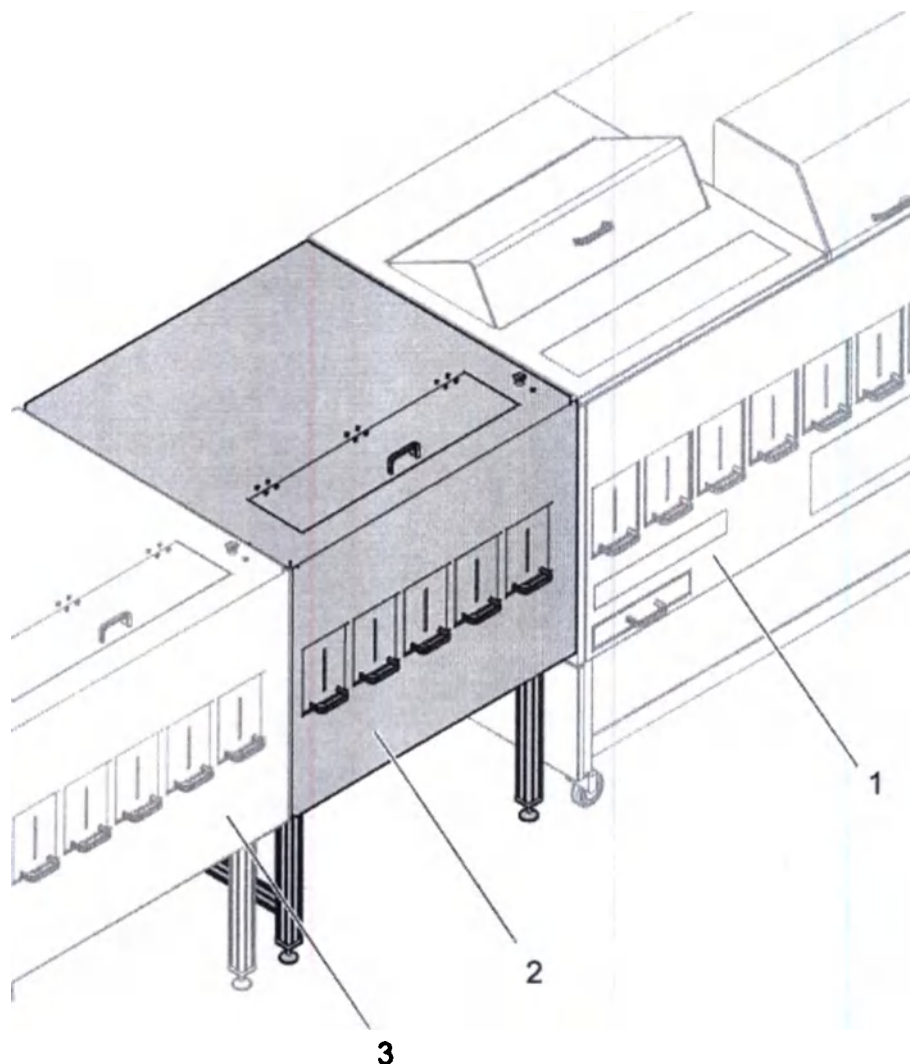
Основное устройство с дополнительными сортировочными модулями
